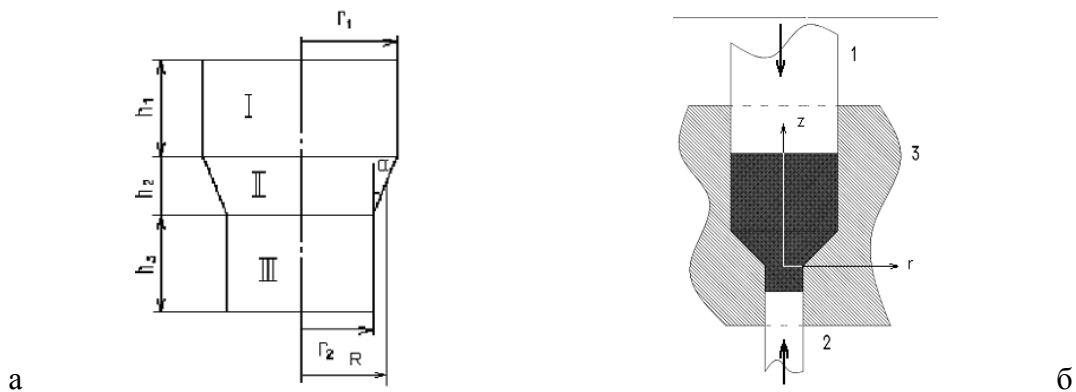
Матриця для ущільнення заготовки: а – схема заготовки, б – схема ущільнення
